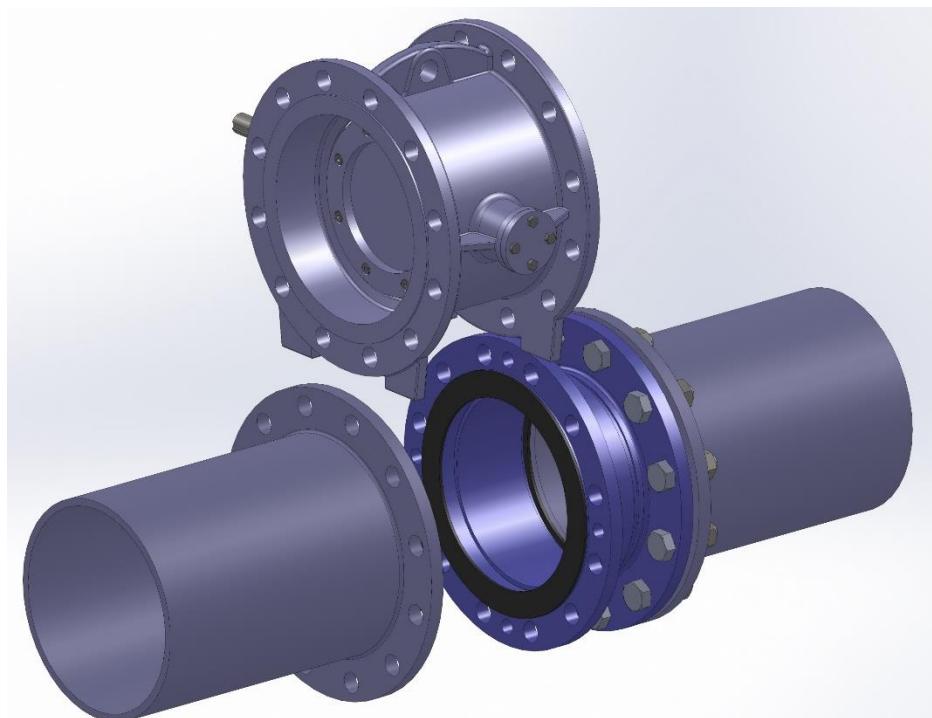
Geleneksel Demontaj Sistemi (Traditional Disassembly Process)
